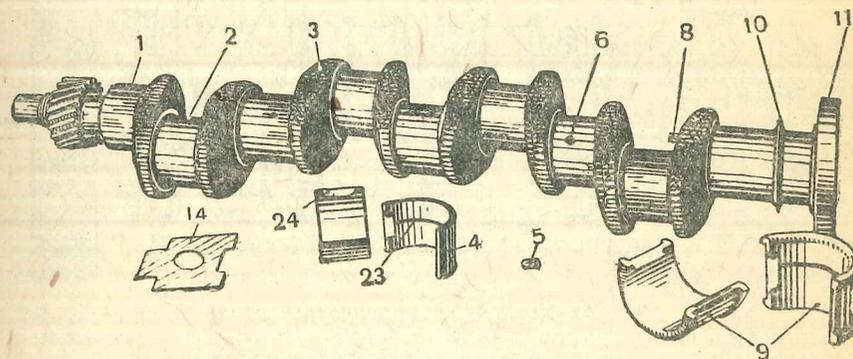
Коленчатый вал и вкладыши коренных подшипников.
